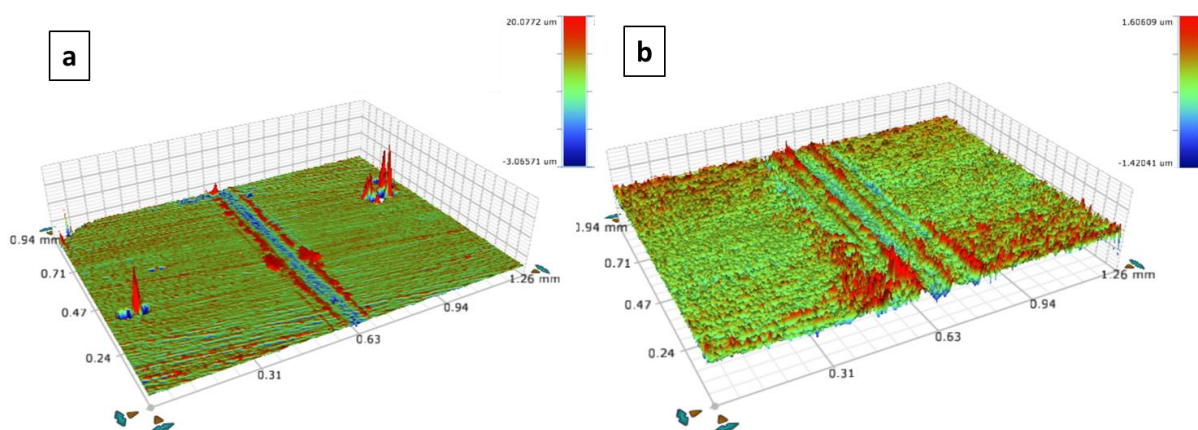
Imagens resultantes da perfilometria no metal de solda do (a) conjunto de similares e do (b) conjunto de dissimilares após ensaio de tribocorrosão.
